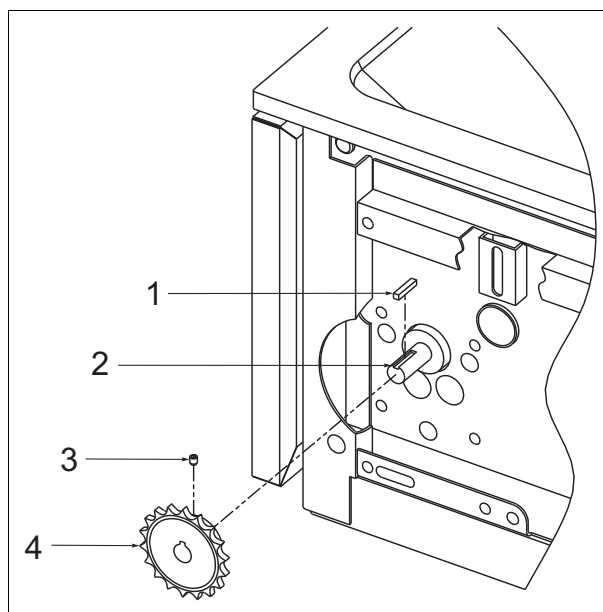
Assemblage de la roue dentée du moto-réducteur
